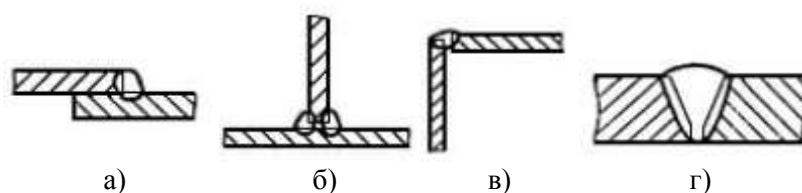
Виды сварных соединений согласно ГОСТ 5264-80:
